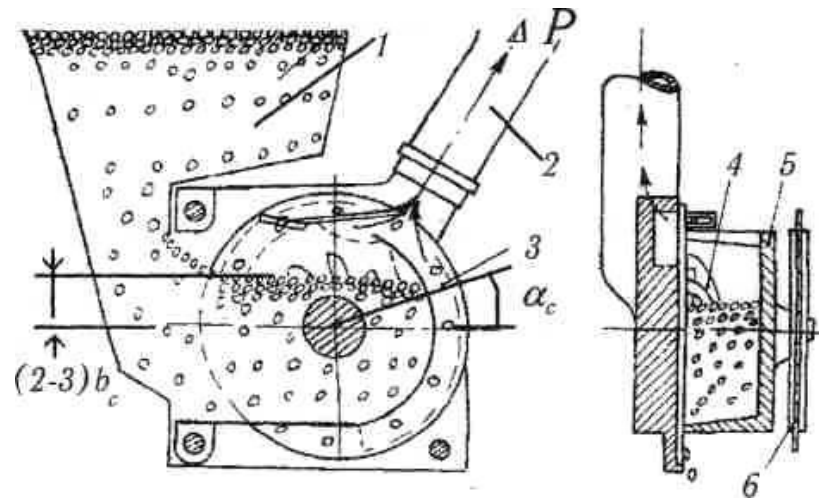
Пневматичний висівний апарат з горизонтальною віссю обертання: 1 – бункер для насіння; 2 – повітропровід; 3 – висівний диск; 4 – ворушилка насіння; 5 – корпус апарата; 6 – ведуча зірочка.
